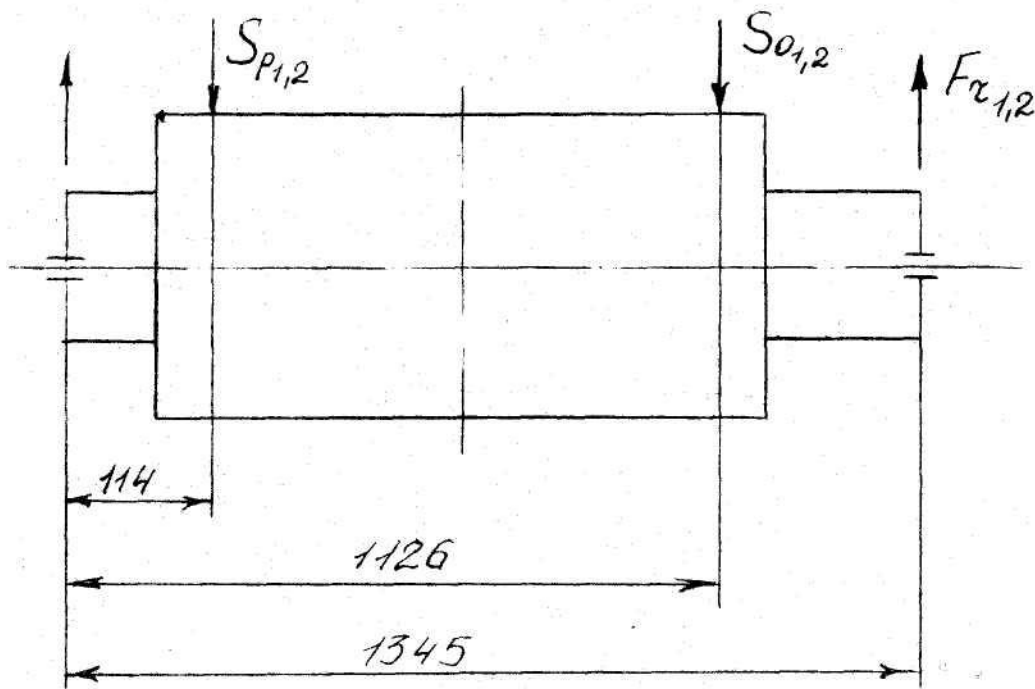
Схема для розрахунку підшипника в опорі барабана
